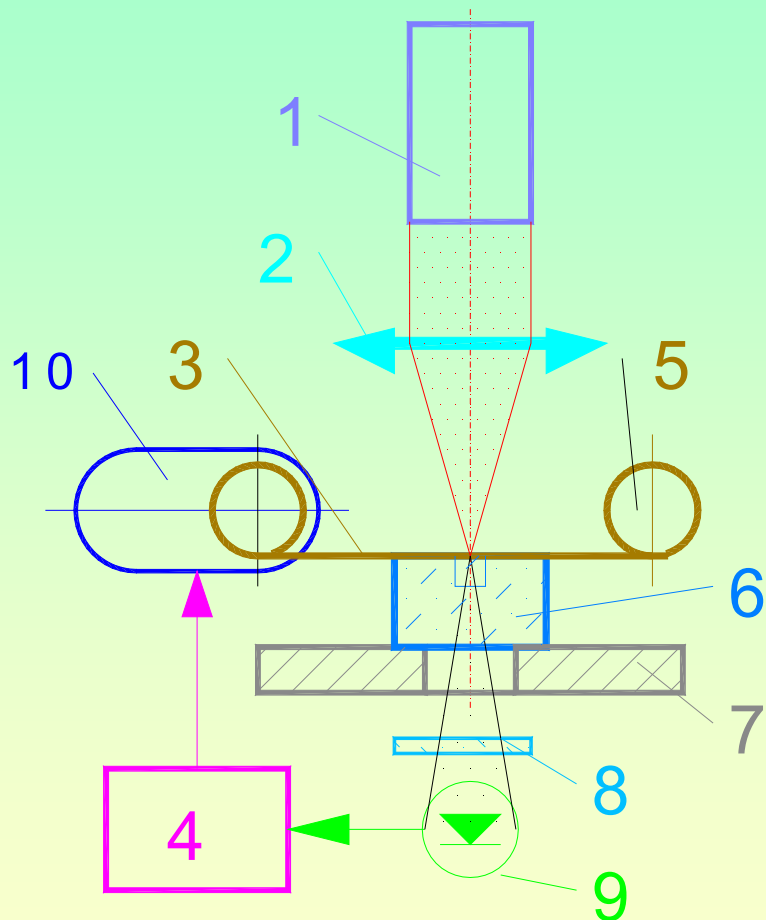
Схема ЛТУ для обробки отворів в заготовках із прозорих матеріалів
